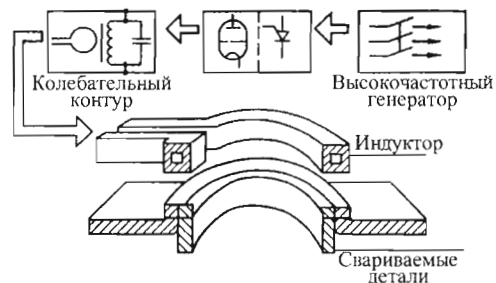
Схема процесса высокочастотной сварки плавлением по отбортованным кромкам
